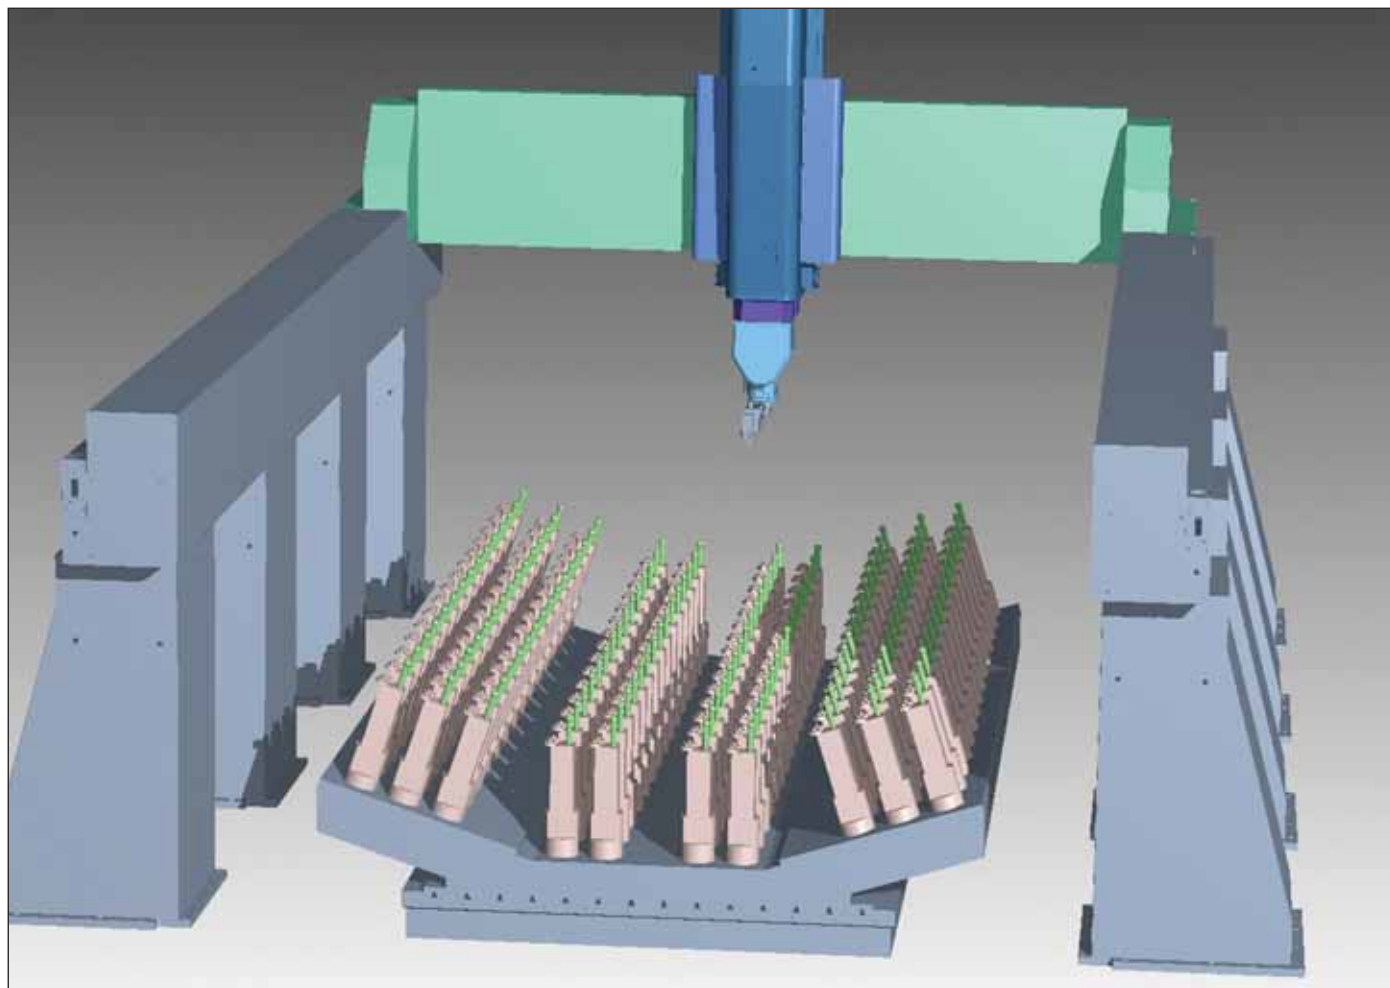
Кинематическая VERICUT-модель станка для обработки листовых деталей
